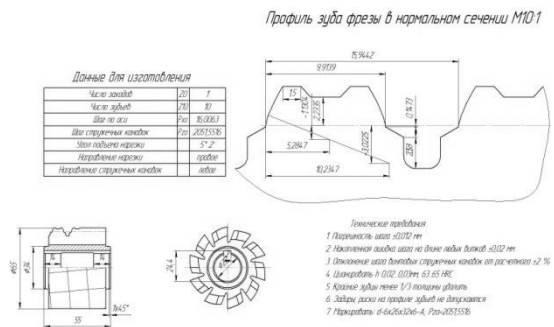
Пример разработки рабочего чертежа червячной шлицевой фрезы
